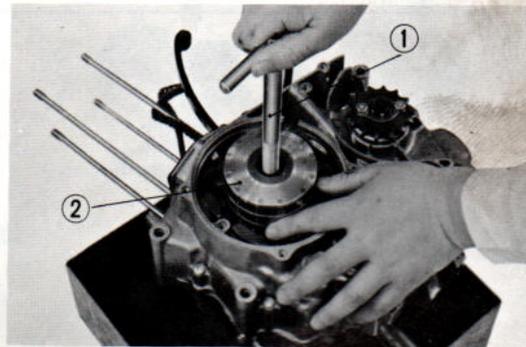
Dépose du rotor ① Extracteur de rotor (Outil n° 07011 . 03001) ② Rotor
